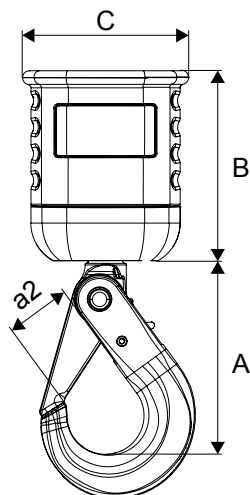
Dimensions du crochet de sécurité à 2 chutes et du moufle
